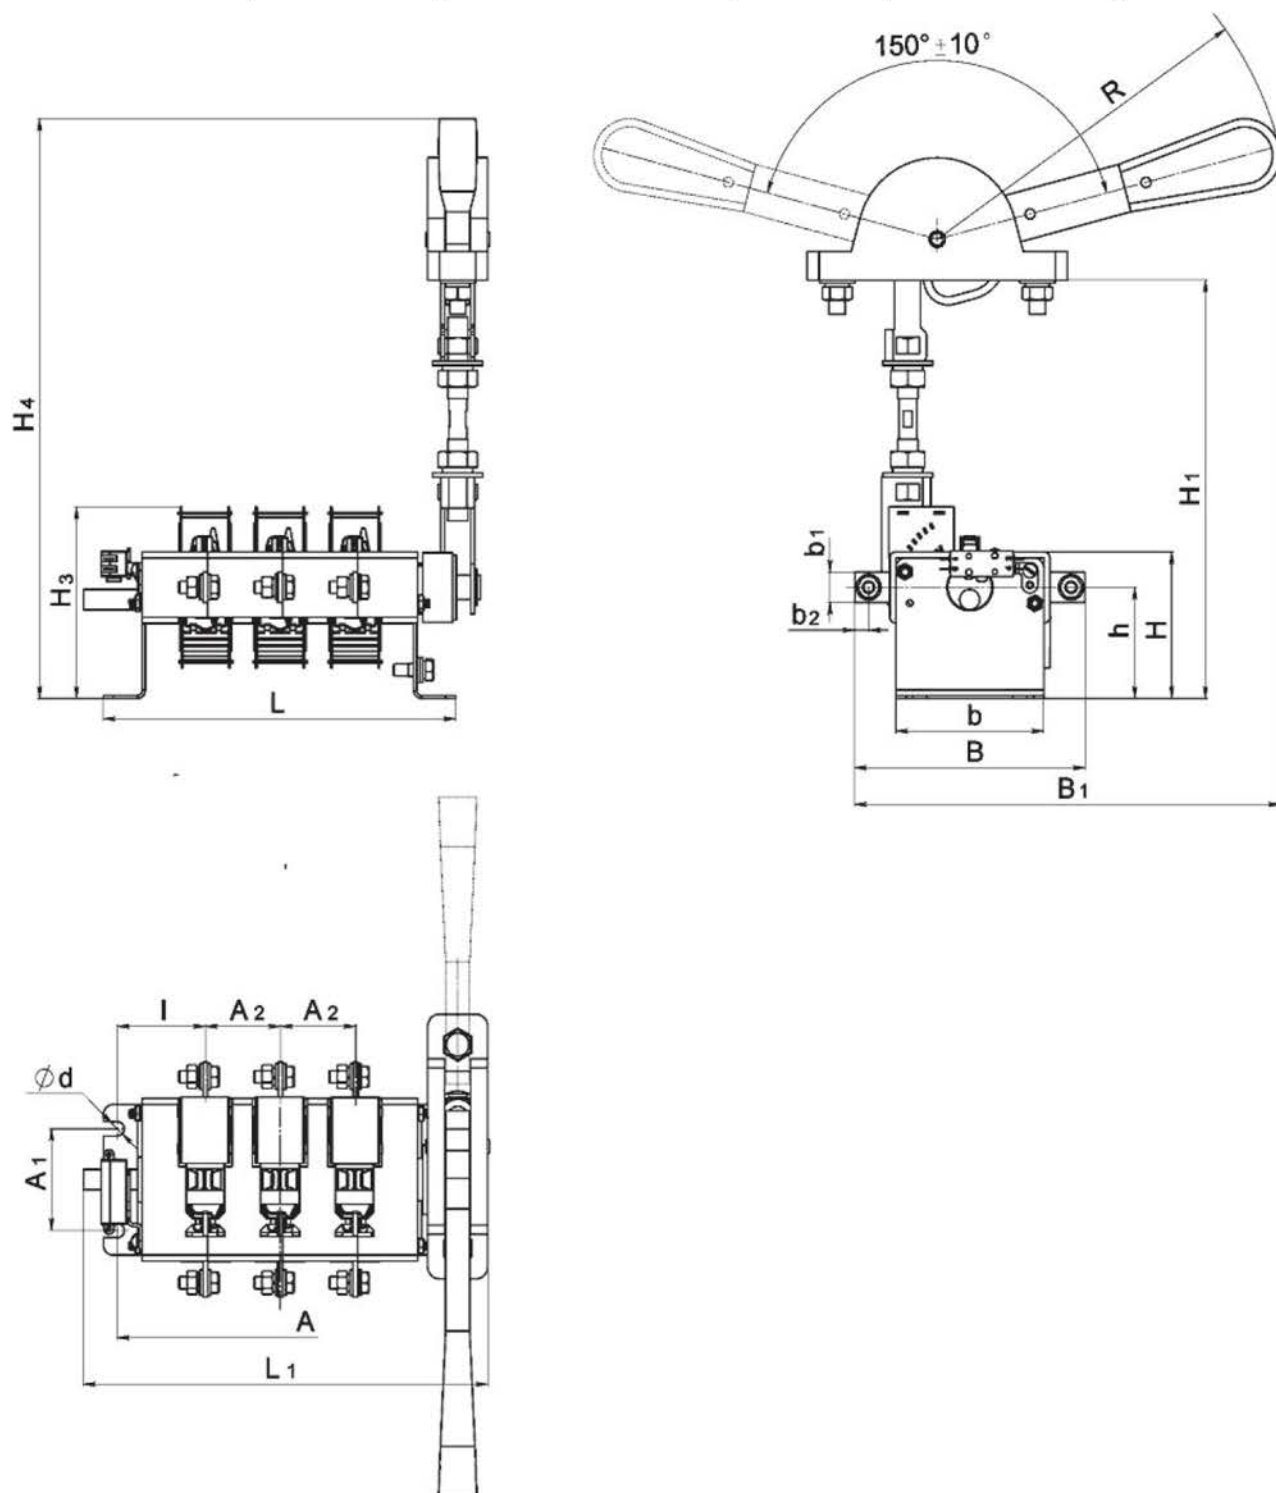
Выключатель-разъединитель трехполюсный на одно направление с передней поворотной рукояткой.
